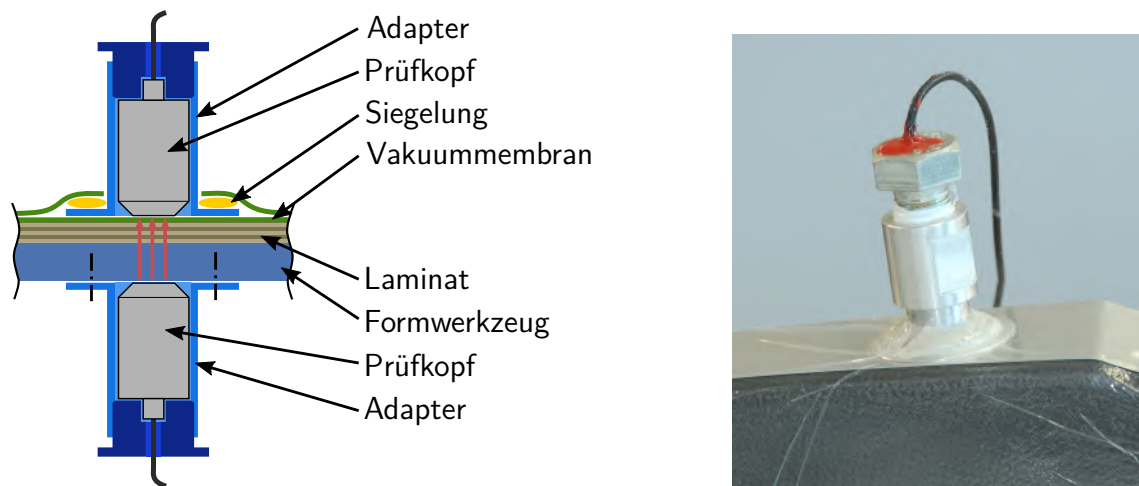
Anpassung der Sensoren auf open-mould-Prozesse
